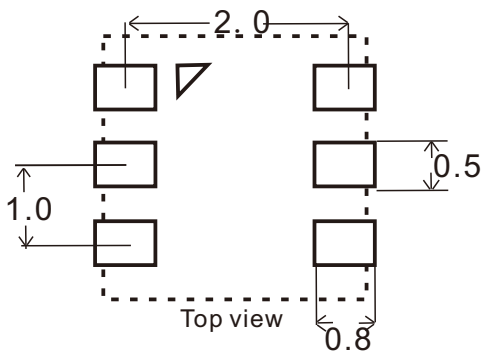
推荐AHT20 PCB设计尺寸（单位：mm），外围虚线部分为SMD封装外部尺寸。
